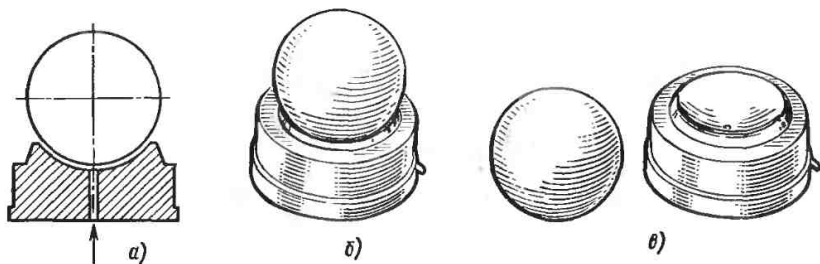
Модель газостатического подшипника: а — разрез; б — общий вид; в — основные детали
